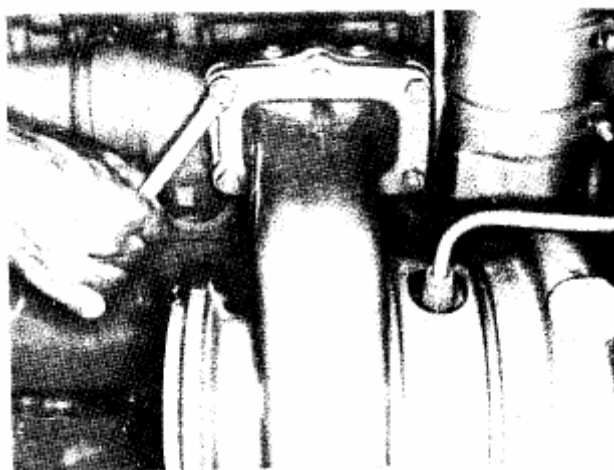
(N11953) Затяжка гаек крепления турбокомпрессора
